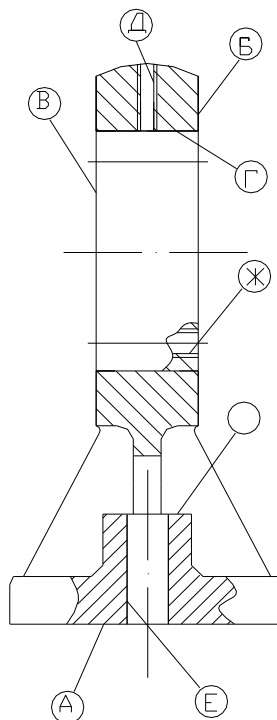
Ескіз корпусу підшипника з позначенням поверхонь
